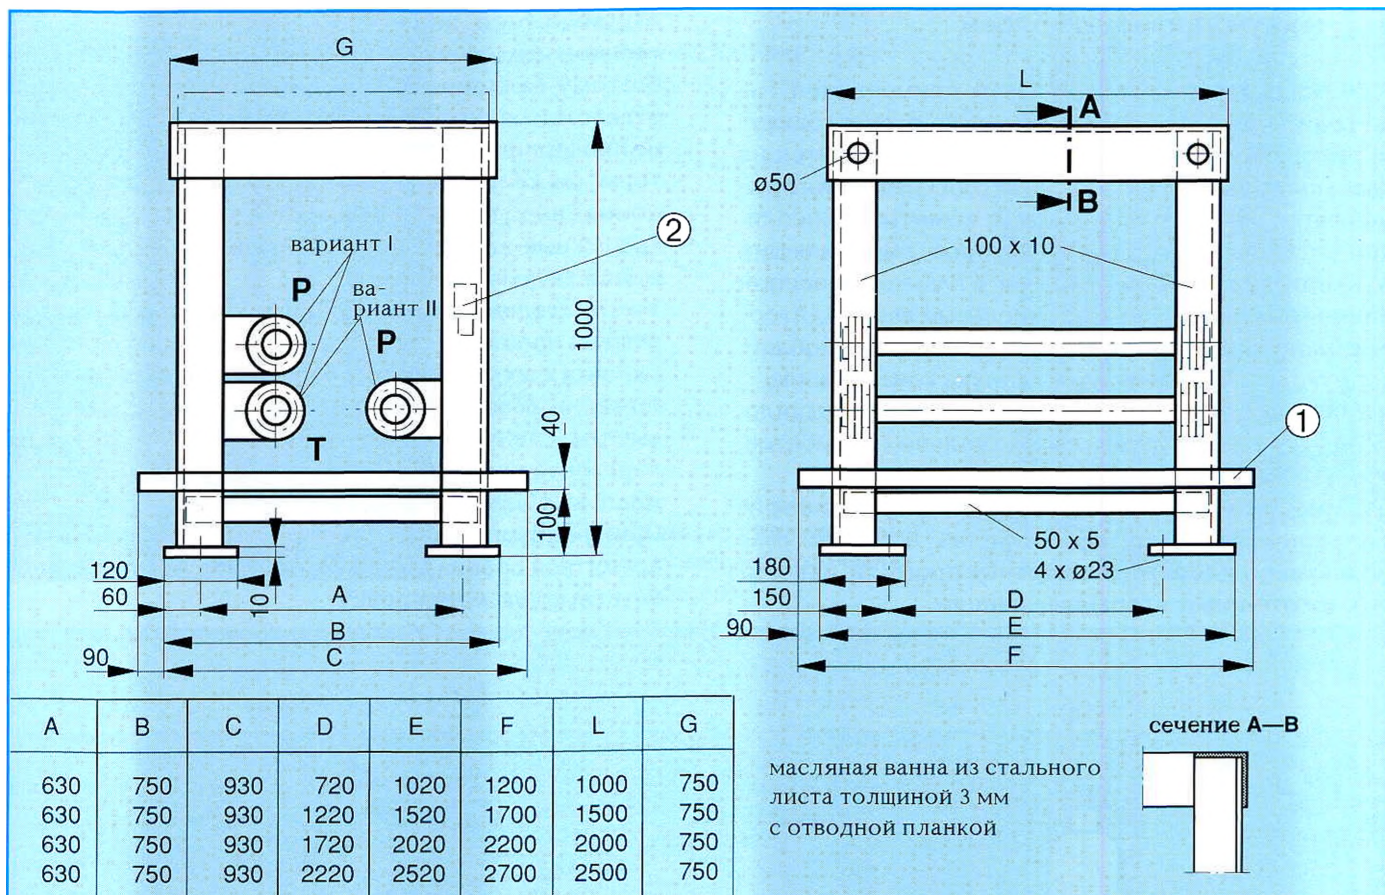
Клапанный стол облегченного типа для установки отдельных клапанов до типоразмера 22 и блоков управления до типоразмера 16
